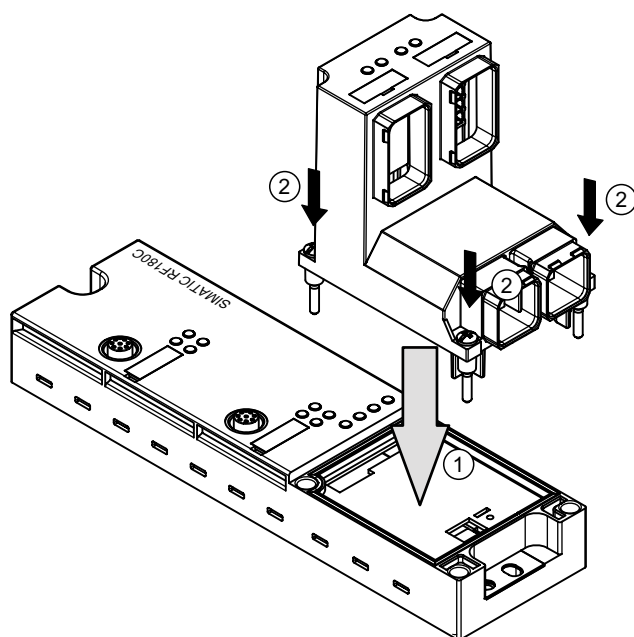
Anschlussblock Push Pull auf das Basisgerät stecken und verschrauben
